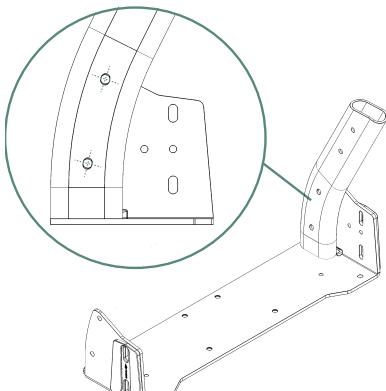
Rahmenteil auf Adapterplatte ausrichten.
